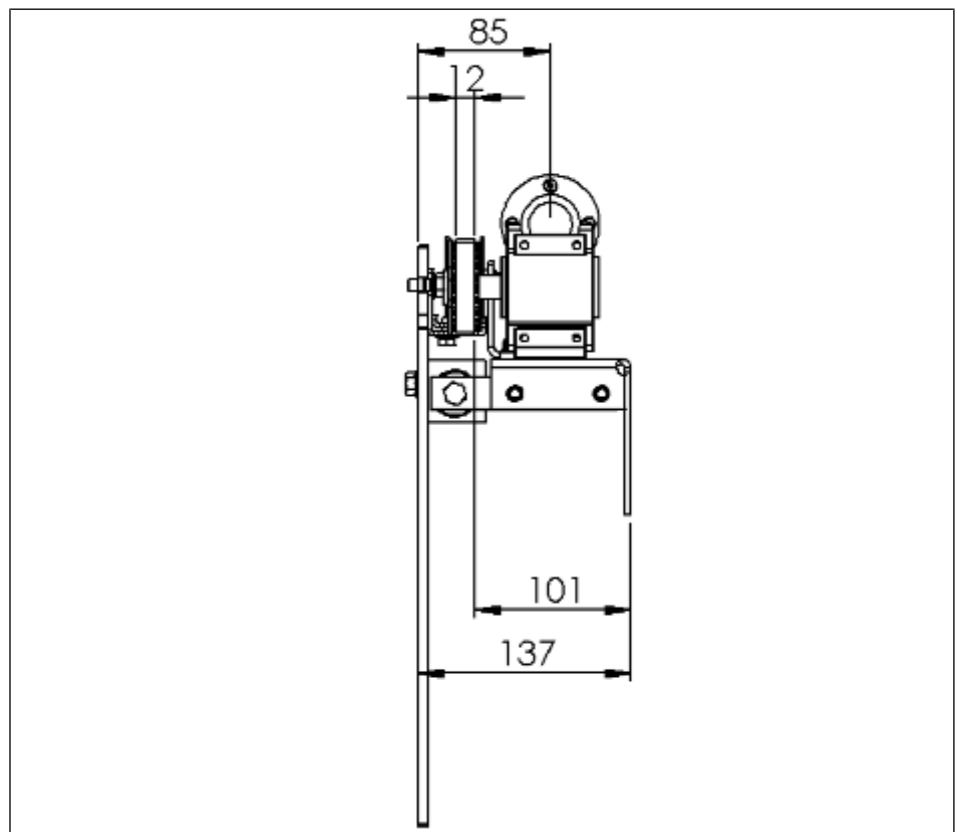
Bemaßung der Mechanik des Türantriebs (Seitenansicht) (Angaben in mm)
